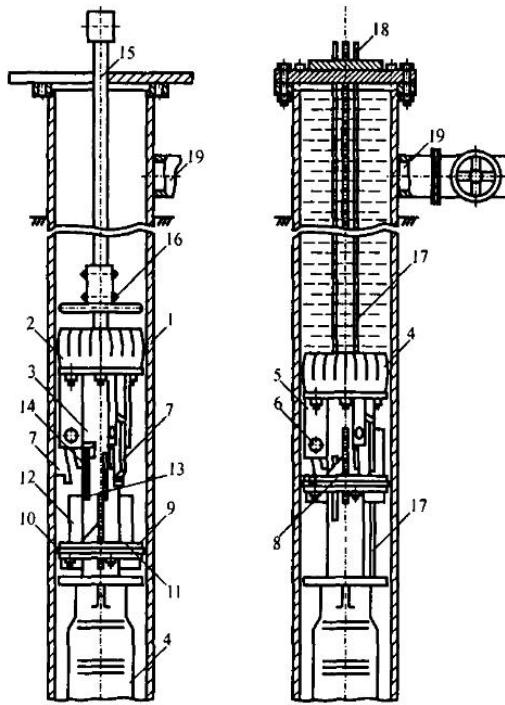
Схема оборудования скважины погружным насосом с беструбной подвеской:
